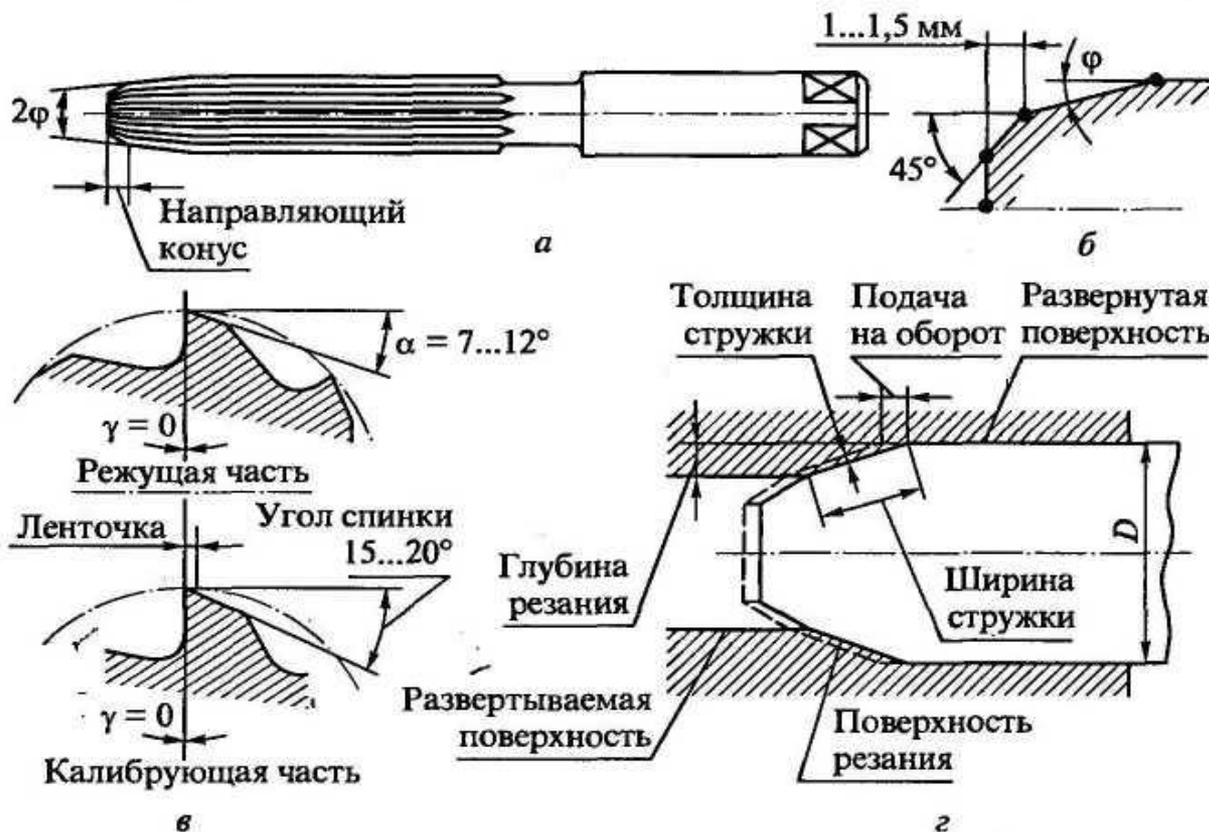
Развертка: а — конструкция; б — конструкция заборной части; в — геометрические параметры режущей и калибрующей частей; г — схема резания; ϕ — угол заборного конуса; 2ϕ — угол при вершине; α — задний угол; γ — передний угол; D — диаметр развертки
